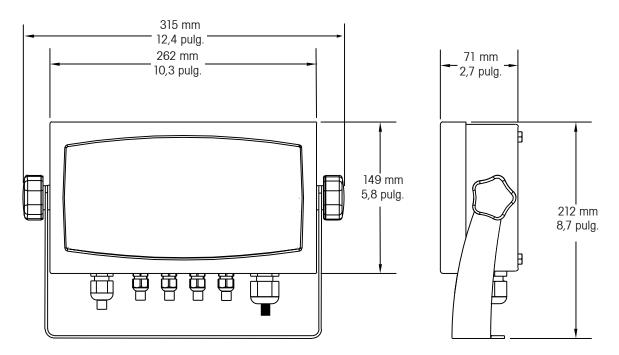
Dimensiones generales del indicador T51XW sin soporte de montaje.
